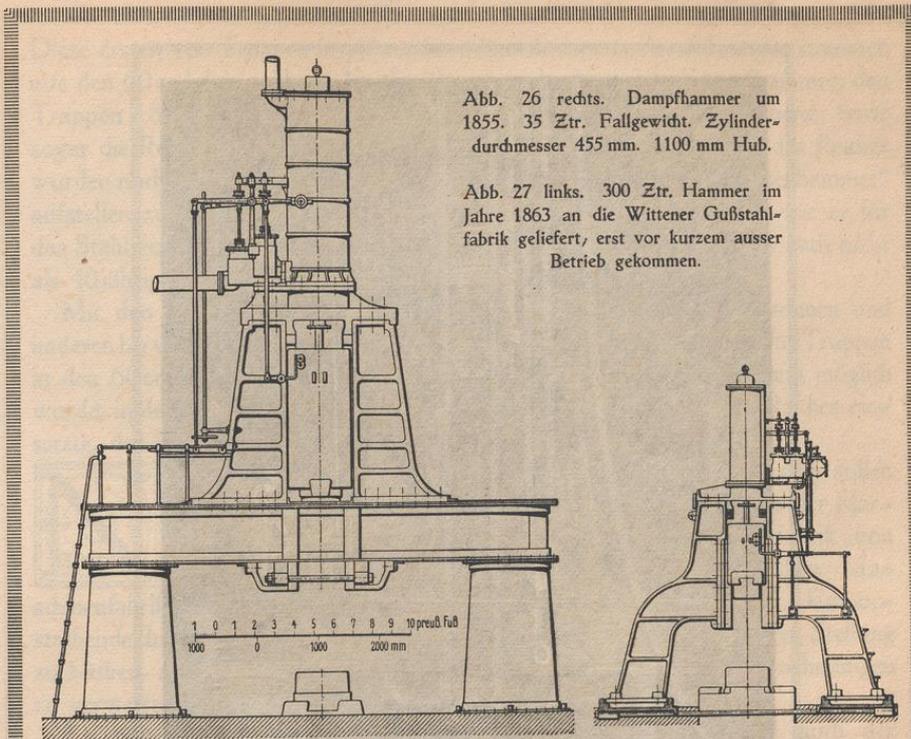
rechts. Dampfhammer um 1855. 35 Ztr. Fallgewicht. Zylinderdurchmesser 455 mm. 1100 mm Hub.
